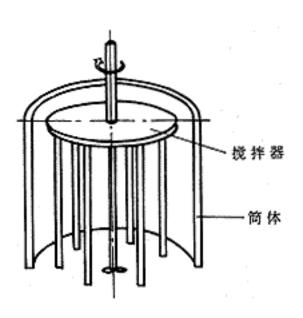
JM1050型搅拌磨机结构示意图 Fig.1 Schematicdrawing of Type JM1050 agitating grinder
